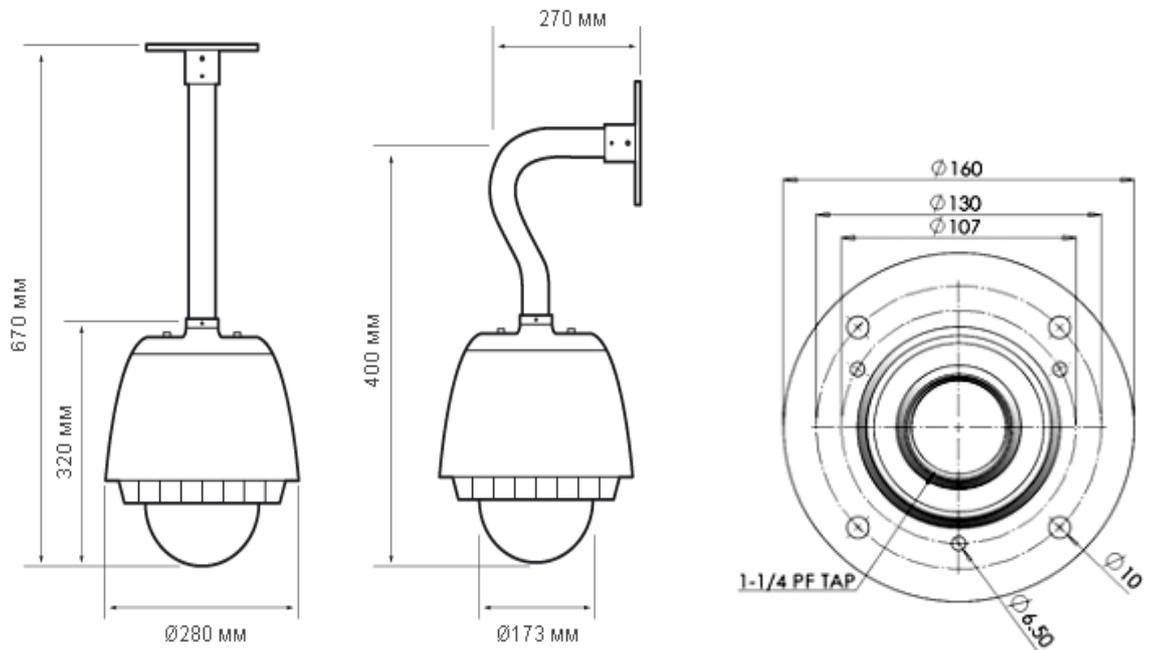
Габаритные размеры поворотной видеокамеры SDP-806С.
